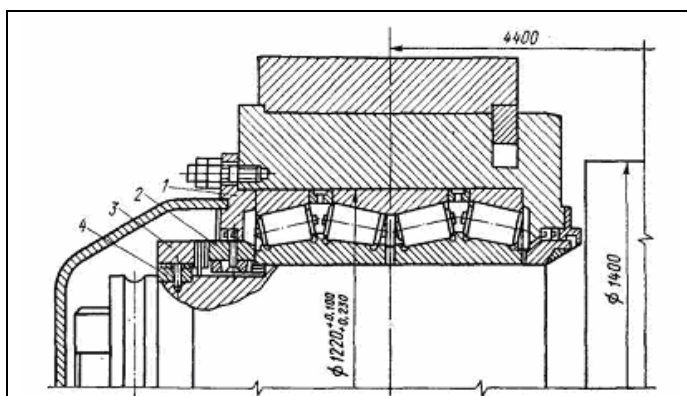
Конструкция подшипникового узла на роликовых конических подшипниках опорного валка стана 2800: 1,2-наружное и внутреннее распорные кольца; 3-кольцо; 4-полукольцо с резьбой
